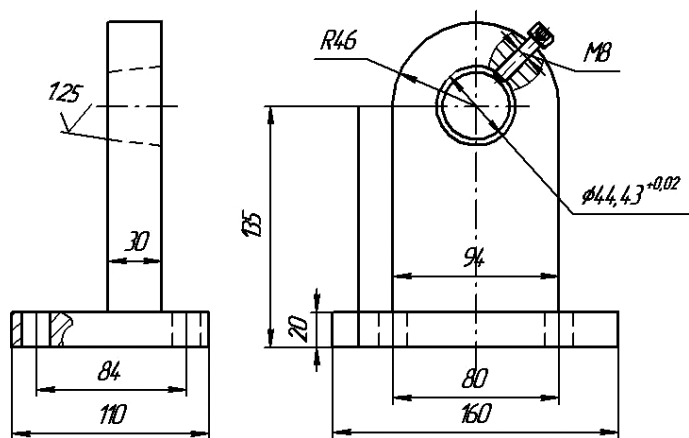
Чертеж приспособления для сборки инструментальной оправки
